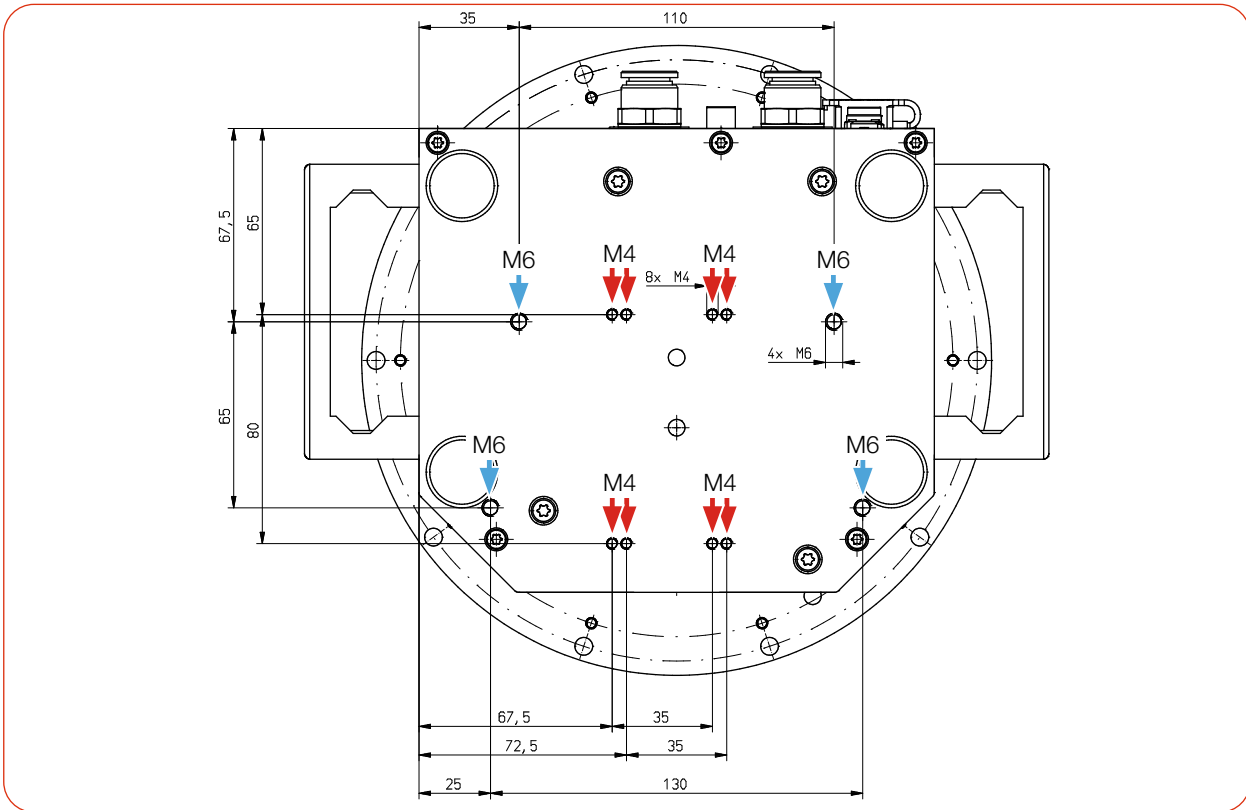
Befestigungsgewinde M4 und M6 im Boden des Gehäuses am CPM+ F-30 (Maße in mm)
